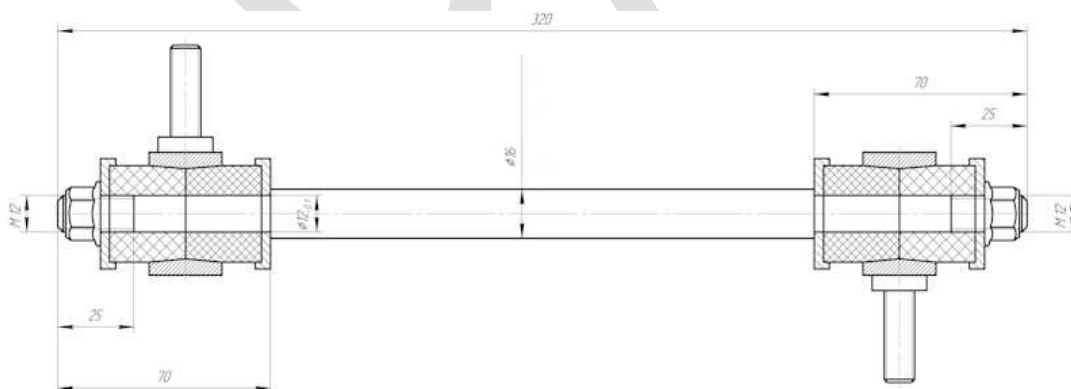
Приклад креслення типової стійки стабілізатору [2]
